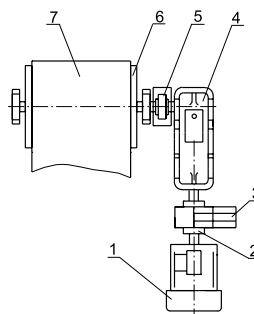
Привод ленточного конвейера на базе коническо-цилиндрического редуктора:
